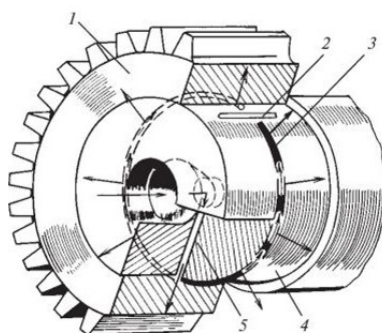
Схема подготовки вала к снятию шестерни
